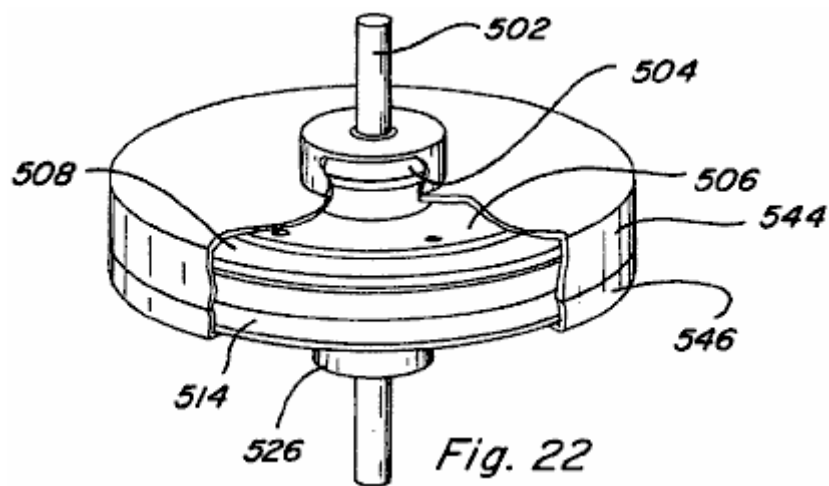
è una vista assemblata in spaccato del dispositivo di moto rotatorio di Fig.19 comprendente una carcassa;
